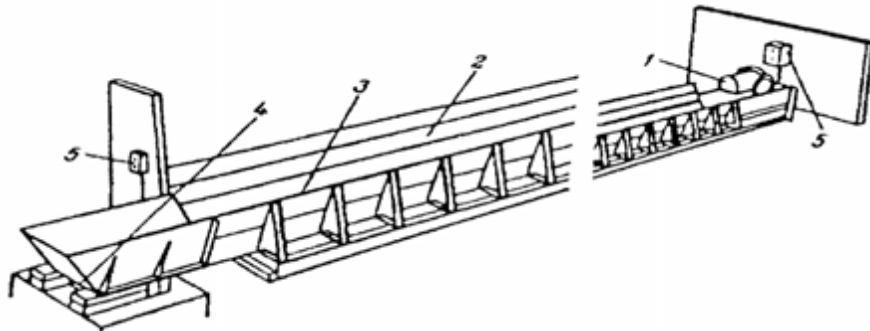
Загальний вигляд скребкового транспортера-роздавача:
